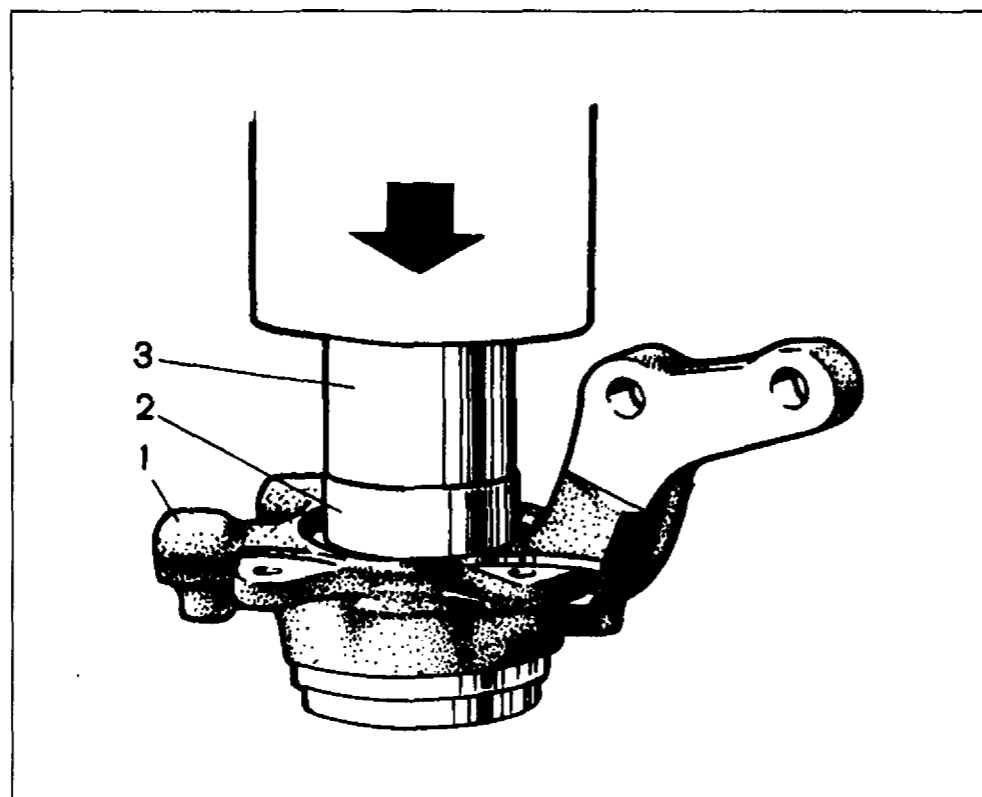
Запрессовка подшипника в поворотный кулак:
